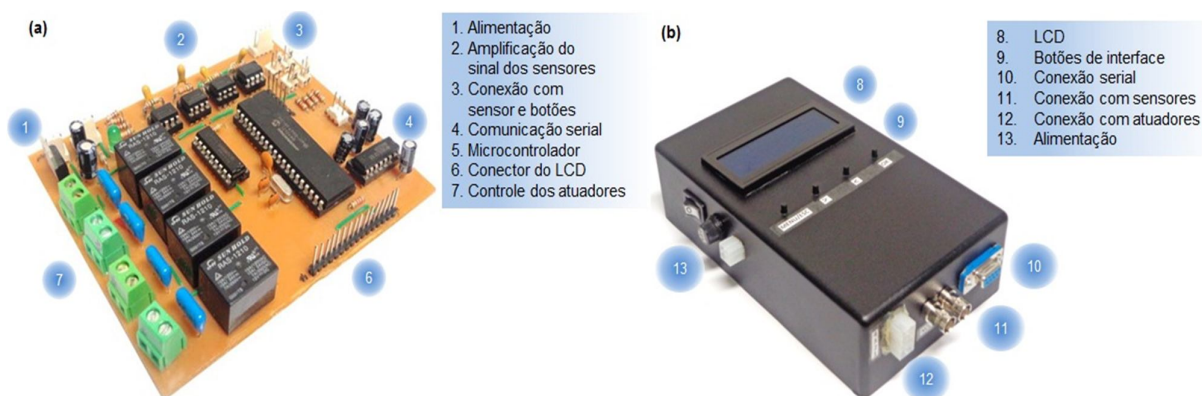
Hardware do dispositivo eletrônico: (a) circuito eletrônico e seus componentes principais; (b) montagem da caixa portátil de proteção.
